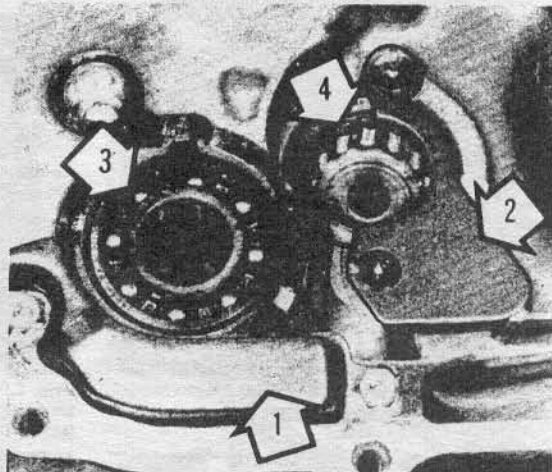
Сборка картера маховика: 1 - сапун; 2 - держатель подшипника; 3 - подшипник вторичного вала; 4 - подшипник промежуточного вала.
